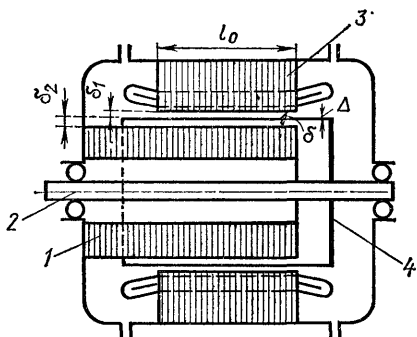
Схема конструкции асинхронного двигателя с немагнитным полым ротором:
